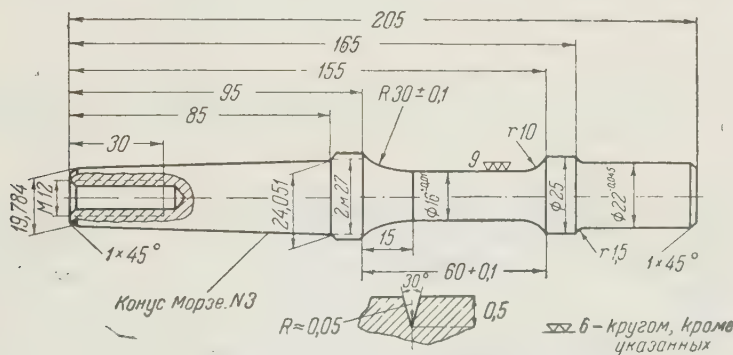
Образец с концентратором напряжения для испытания на усталость
